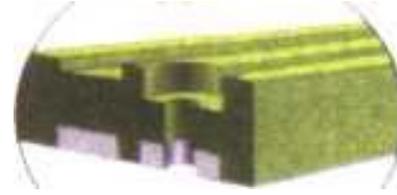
Установка и пайка ЭРИ с круглыми штыревыми выводами в сквозное круглое монтажное отверстие
